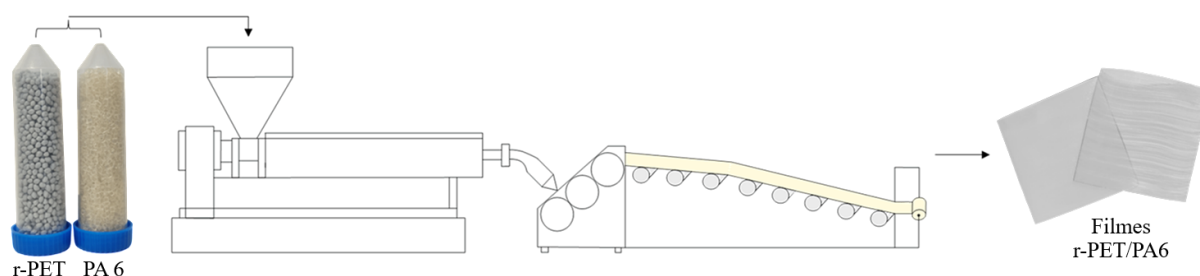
Esquema de extrusão seguida de moldagem de filmes com bobinamento por calandras
